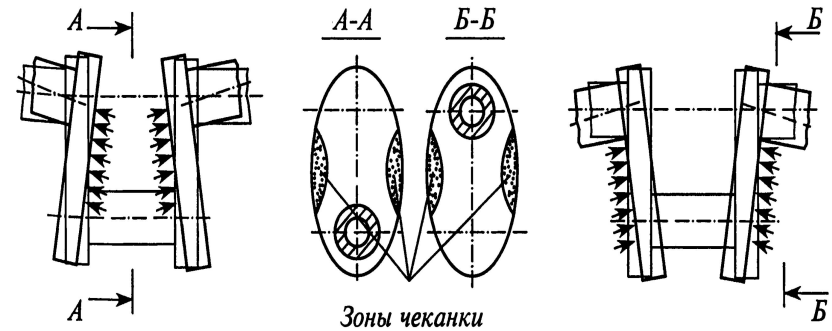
Правка коленчатого вала наклепом (*чеканкой*)
